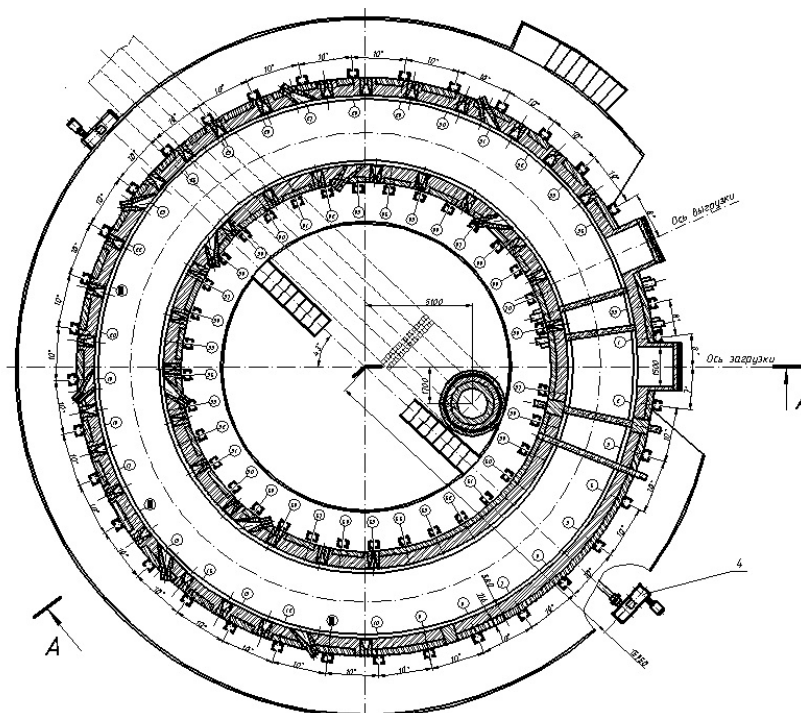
Кольцевая печь для нагрева заготовки перед раскроем ТПЦ-2 ОАО «ЧТПЗ»
